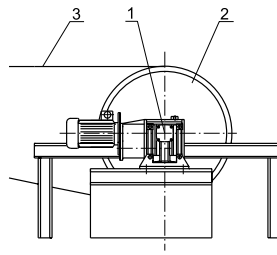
Привод ленточного конвейера на базе червячного редуктора:
